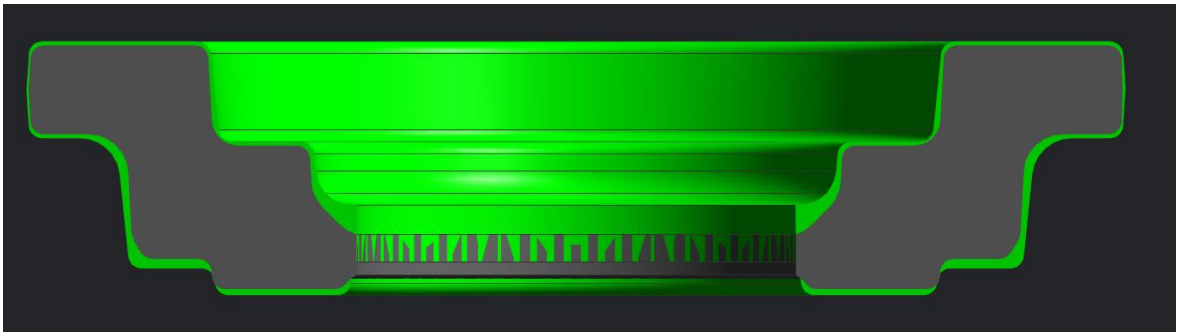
Dokovací zápusťky spodní a horní po odkování 1500 kusů
